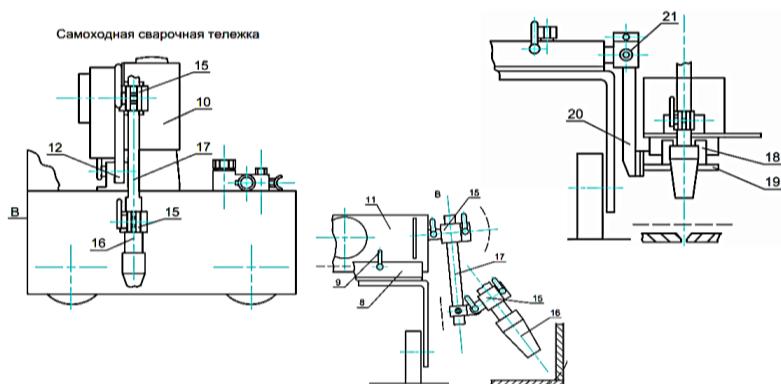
Общая конструкция самоходной сварочной тележки для автоматизированного мобильного технологического комплекса сварки
